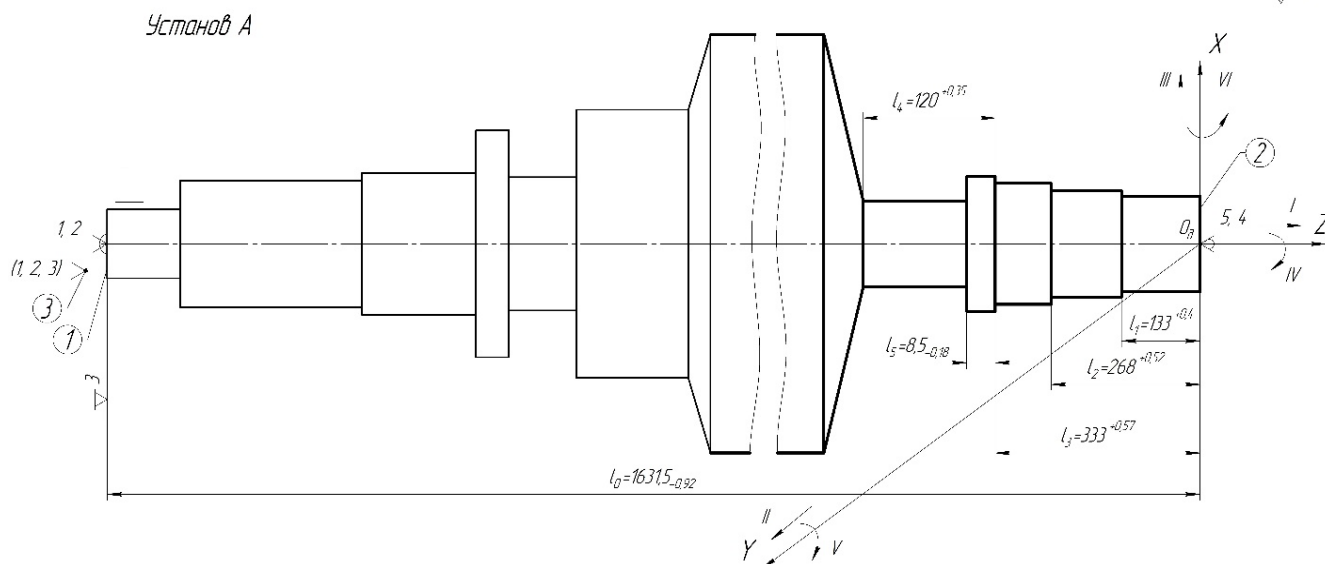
Схеми установки заготовки на операції 020. Цифри в дужках – другий (альтернативний) варіант установки заготовки
